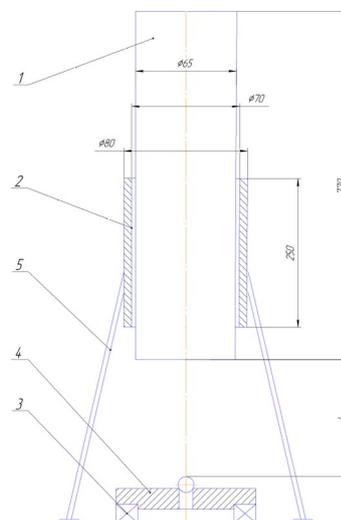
Схема установки для испытания подшипника на сопротивление ударной нагрузке
